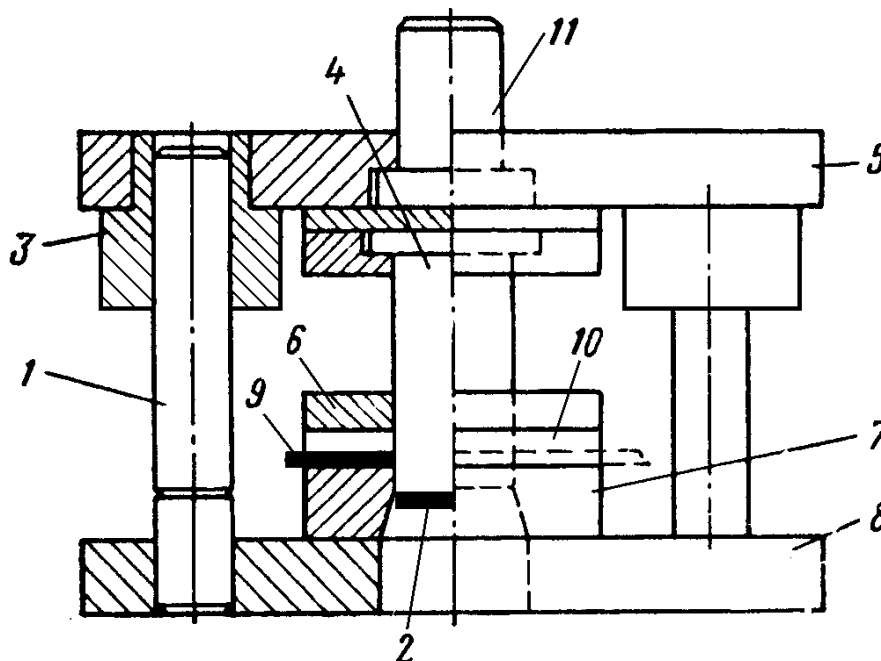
Штмп із напрямними колонками: 1 – напрямні колонки; 2 – готова деталь; 3 – напрямні втулки; 4 – пуансон; 5 – верхня плита; 6 – знімач; 7 – матриця; 8 – нижня плита; 9 – смуга; 10 – напрямні планки; 11 – хвостовик
